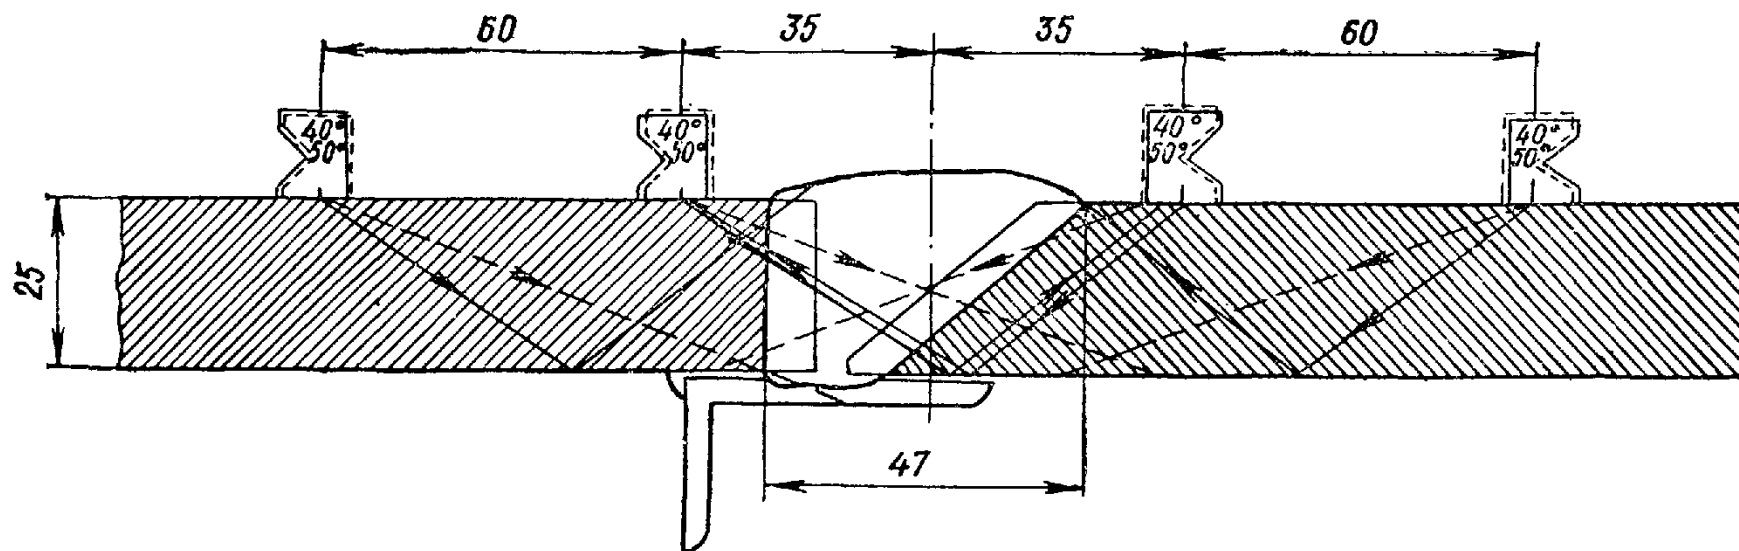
Схема контроля стыкового сварного шва в стали толщиной 25 мм
